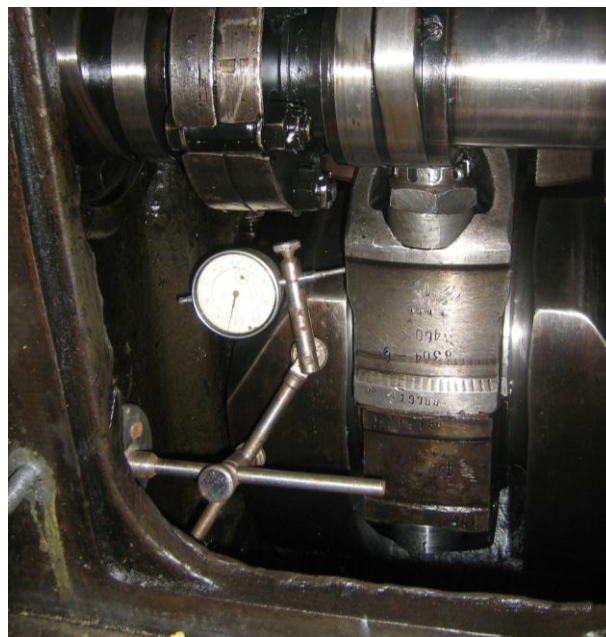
Установка индикатора для замера разбега ШПГ
